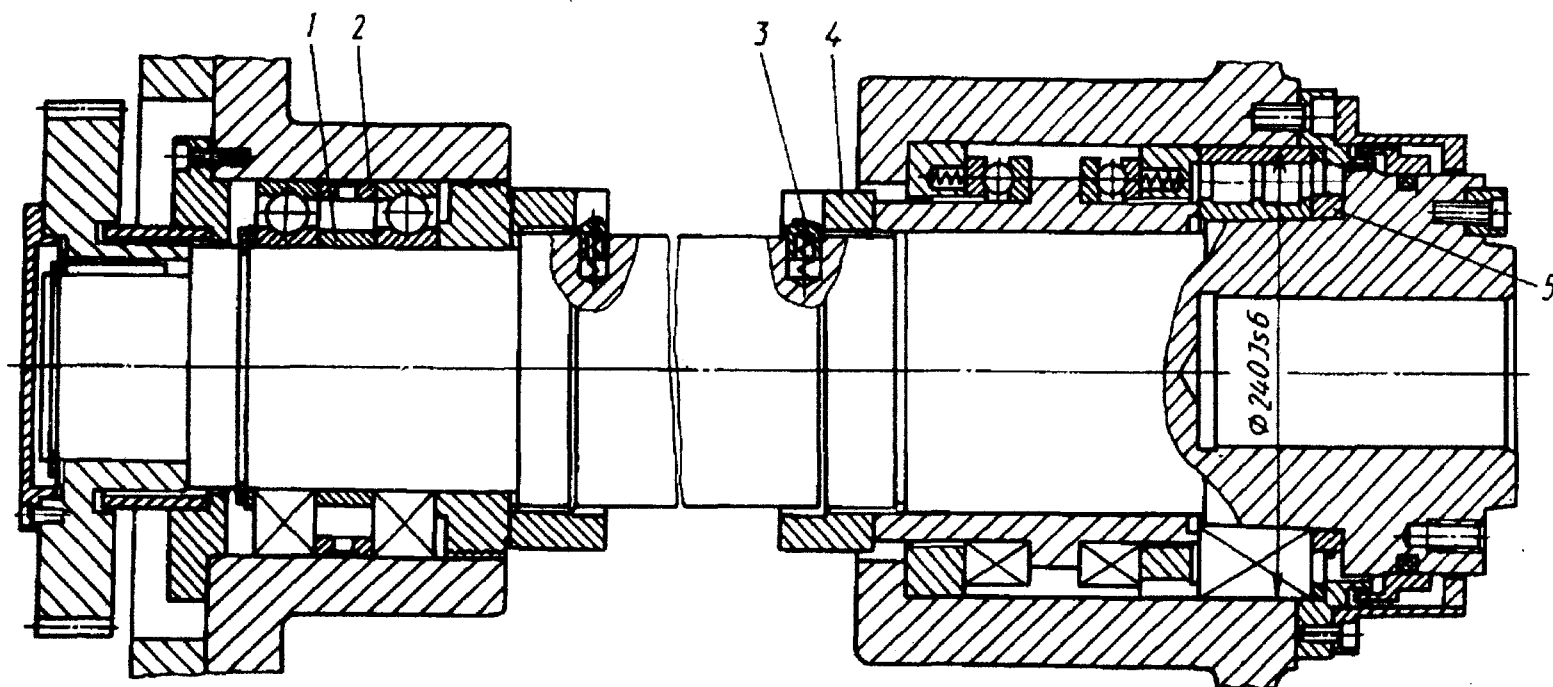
7. Шпиндельный узел расточной бабки агрегатного станка :
